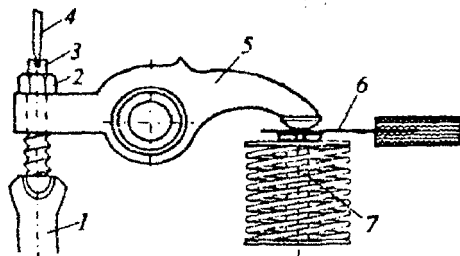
Регулировка зазоров в газораспределительном механизме с нижним расположением распределительного вала: 1 – штанга; 2 – контргайка; 3 – регулировочный винт; 4 – отвертка; 5 – коромысло; 6 – шуп; 7 – клапан
